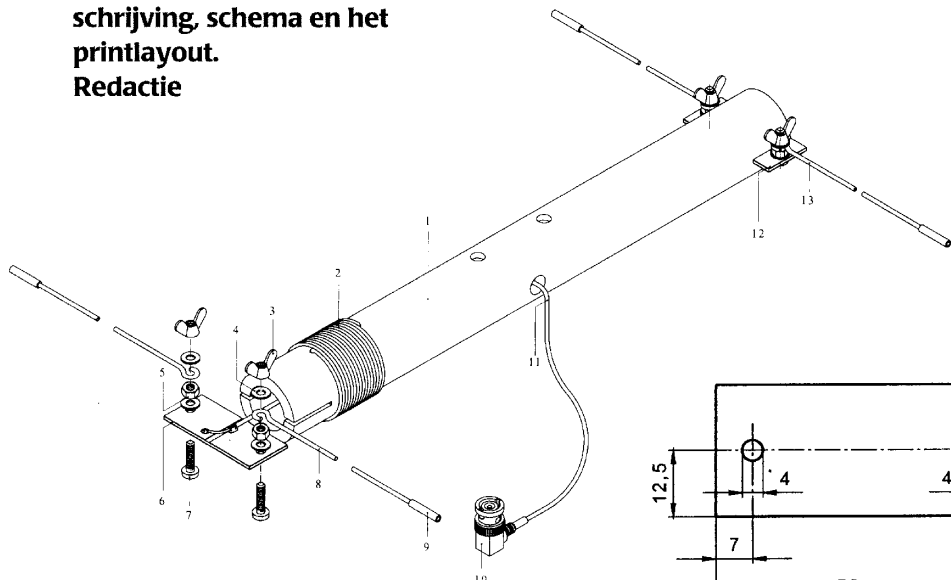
Exploded view van de peilantenne. De coaxkabel wordt ook gebruikt om de juiste aanpassing te verkrijgen.
